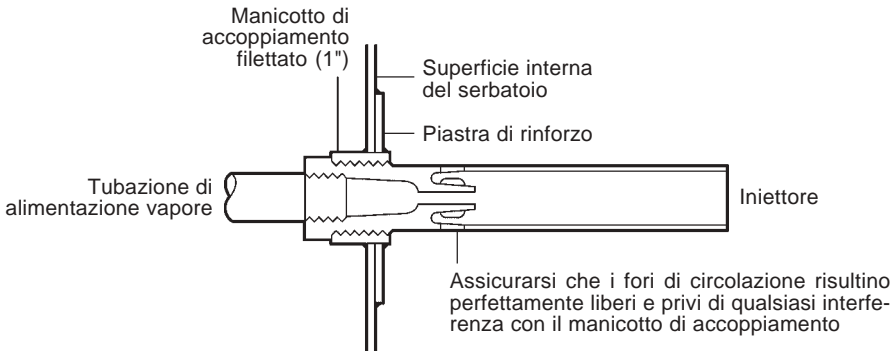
Iniettori IN15 - Tipica installazione con montaggio a parete del serbatoio
